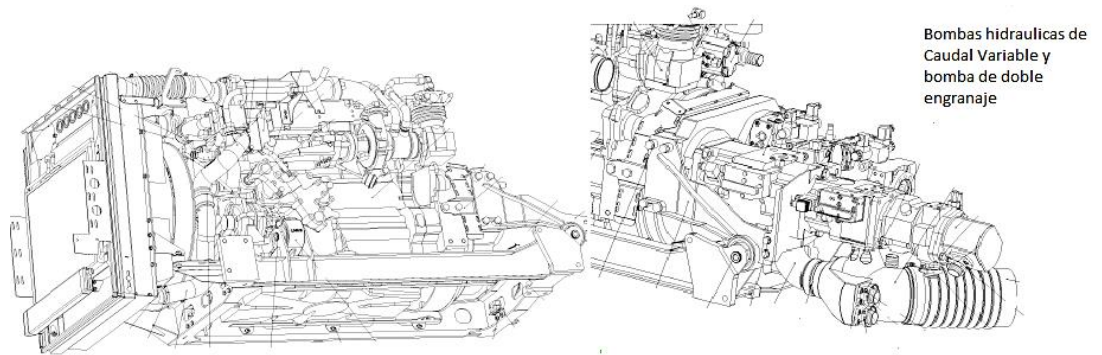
Conjunto Motor y Bombas Hidráulicas de la Grúa.
